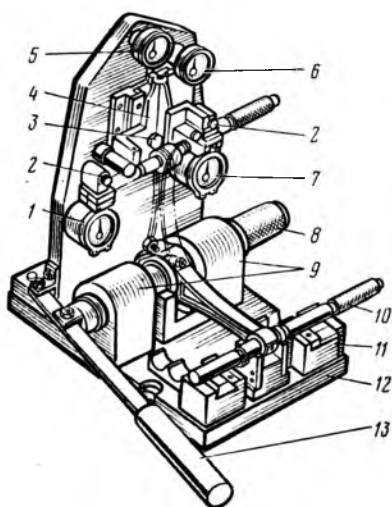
Приспособление для проверки межцентрового расстояния и параллельности осей отверстий в головках шатуна:
